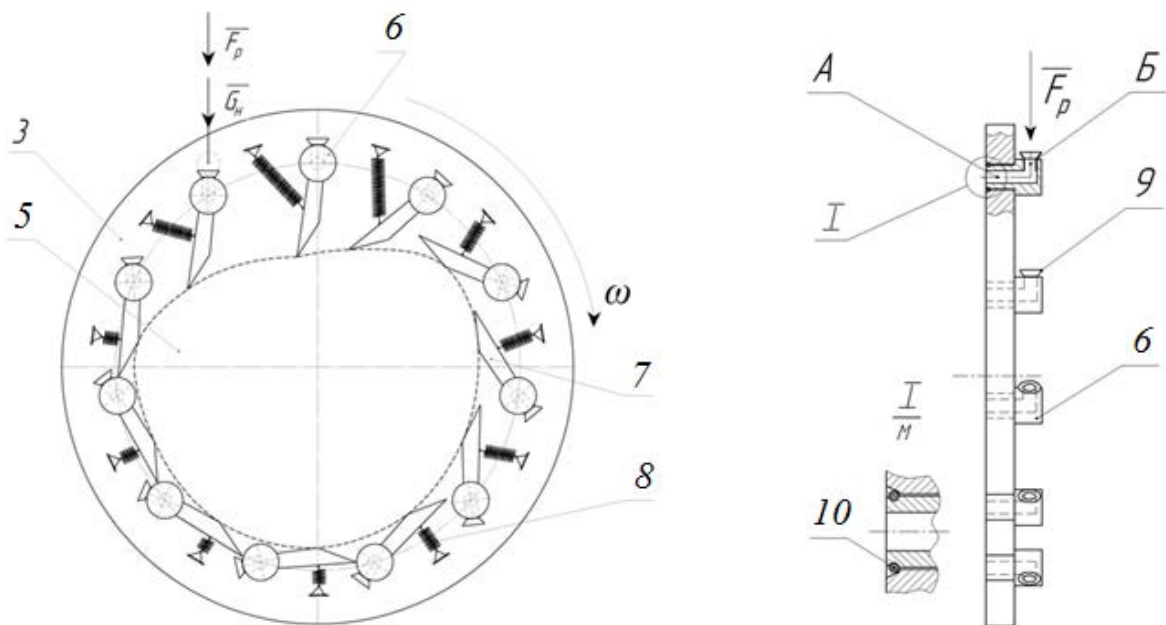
Дозатор насіння з активними комірками: 6 – поворотна комірка; 7 – важіль; 8 – пружина; 9 – сопло; 10 – стопорне кільце; А – осьове свердлення поворотної комірки; Б – радіальне свердлення поворотної комірки;  $\overline{F_p}$  – присмоктувальна сила;  $\overline{G_H}$  – сила тяжіння насінини.
